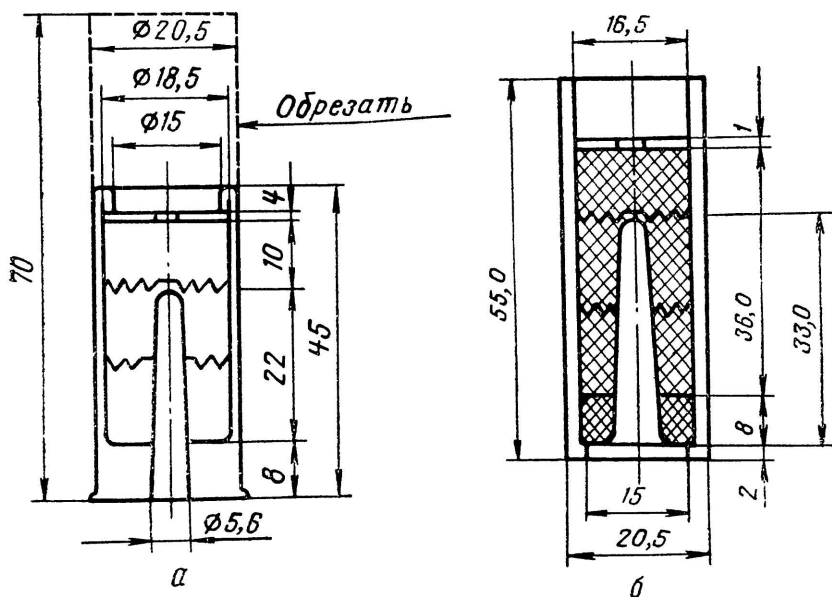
Модельный ракетный двигатель ДБ-51-С-10: а—в охотничьей гильзе 12-го калибра; б—в трубке с керамическим соплом
